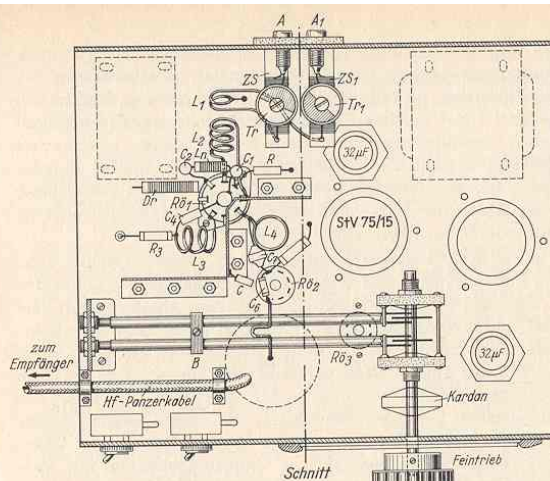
Konstruktionszeichnung für den Kaskoden-Konverter, Ansicht von unten. Maßstab 1 : 3
